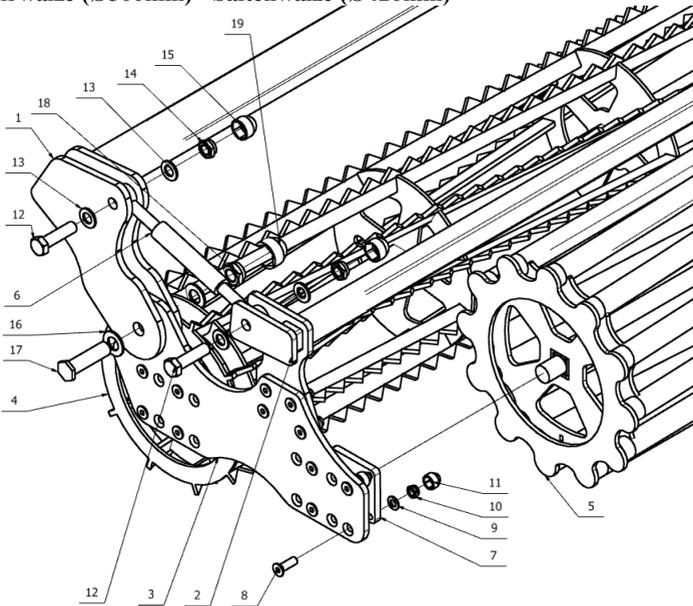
Tandemrolle Rohr (Ø500mm) - Strang (Ø420mm).
